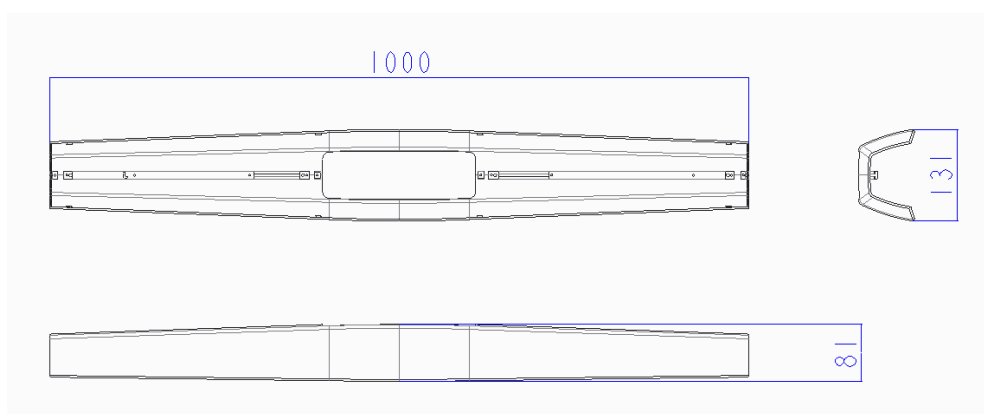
Hrubá stavební struktura – Varianta A s rozměry
